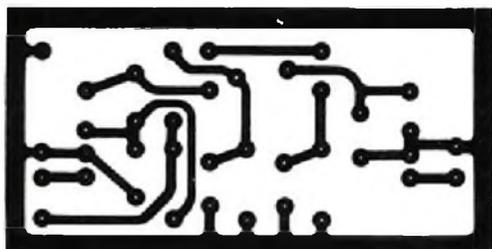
Placa de circuito impresso vista do lado cobreado.
